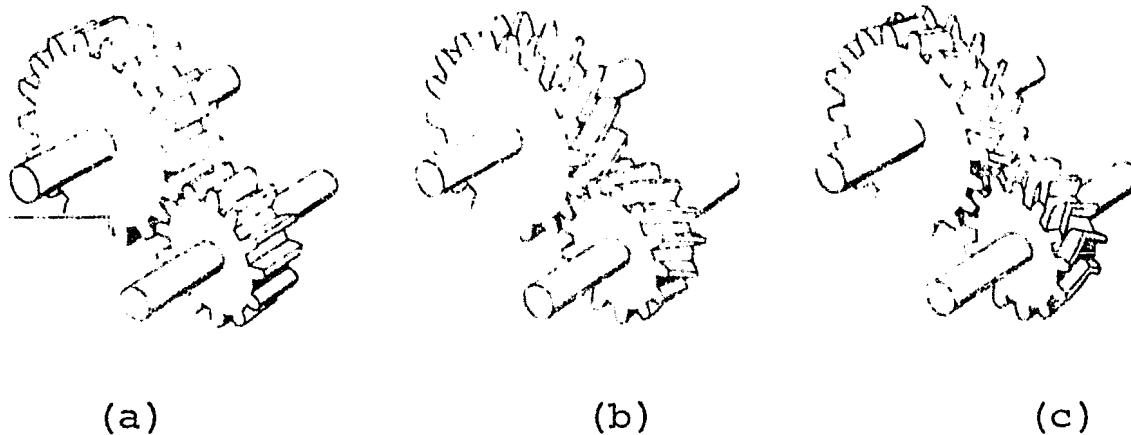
Engranajes de ruedas frontales. (a) Ruedas frontales con dientes rectos; (b) Ruedas frontales con dientes inclinados; (c) Ruedas frontales con dientes en forma de flecha.
